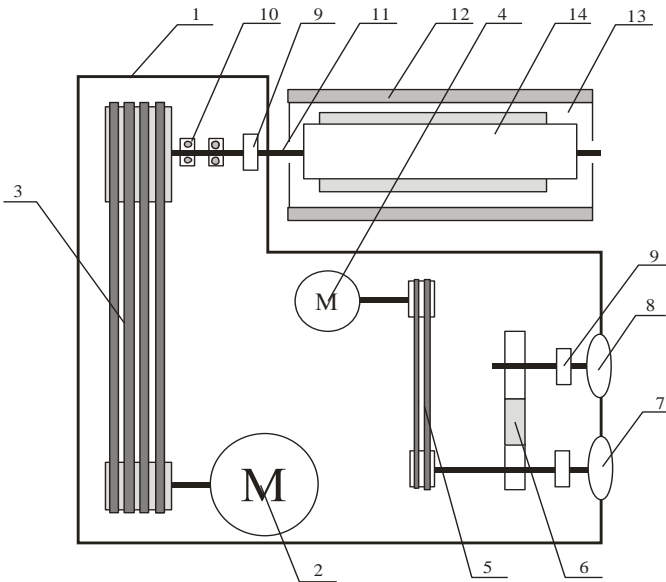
Кінематична схема фризера: 1 – станина; 2 – електродвигун мішалки; 3 – клинопасова передача; 4 – електродвигун приводу насосів; 5 – клинопасова передача; 6 – редуктор; 7 – насос першого ступеню; 8 – насос другого ступеню; 9 – муфта; 10 – підшипники; 11 – вал мішалки; 12 – охолоджувальна сорочка; 13 – циліндр; 14 – мішалка
